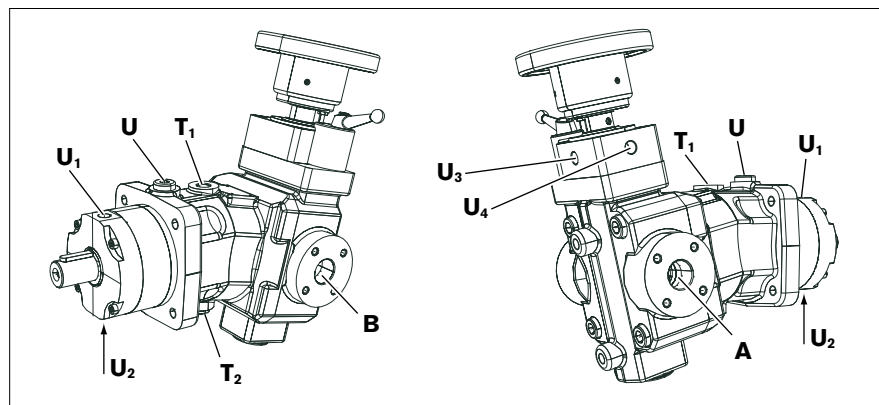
Vue d'ensemble des raccords A7VK, modèle à circuit fermé
